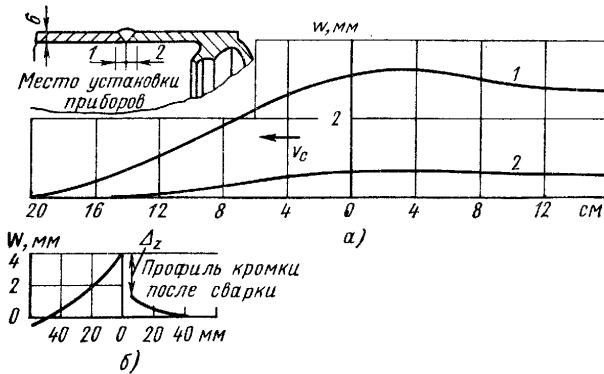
Перемещения w в зоне кольцевого шва цилиндрической оболочки из алюминиевого сплава:
